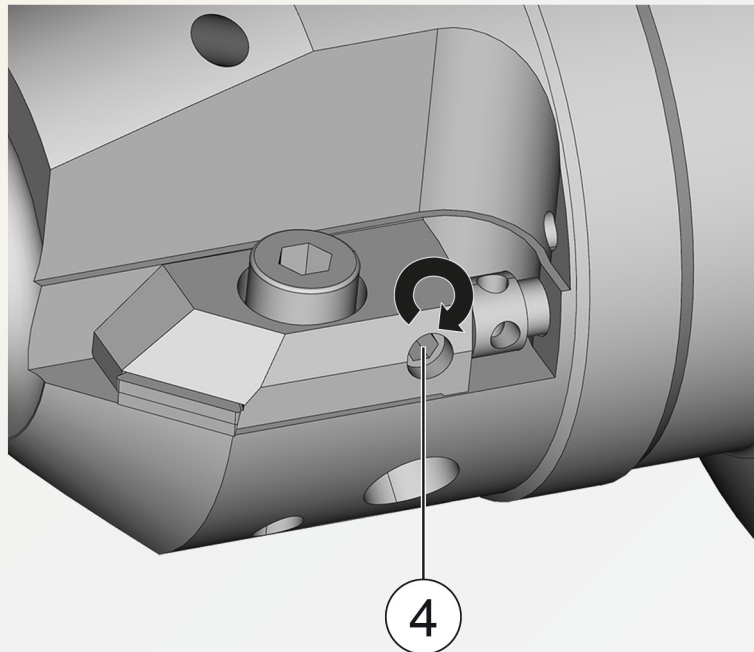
Winkel mit der Winkeleinstellschraube auf Sollmaß einstellen
